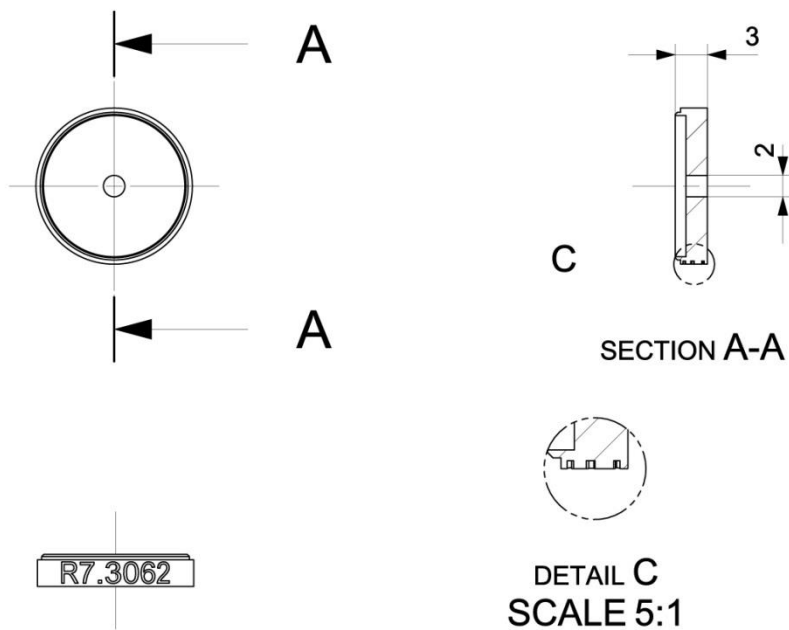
Technische Zeichnung Kappchen für Aktormodulgehäuse V02T08
